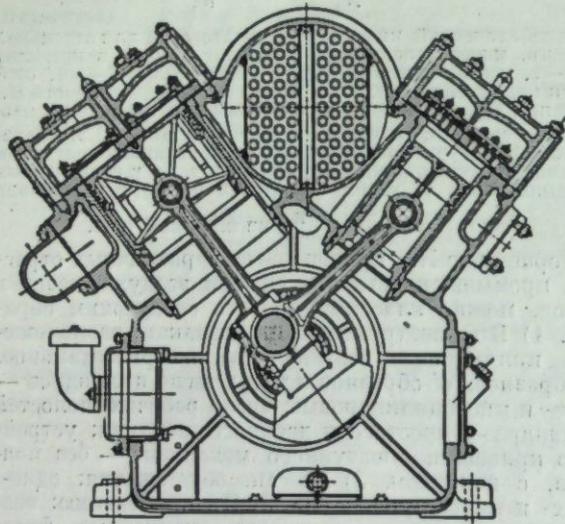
V-образный поршневой двухступенчатый компрессор простого действия.
